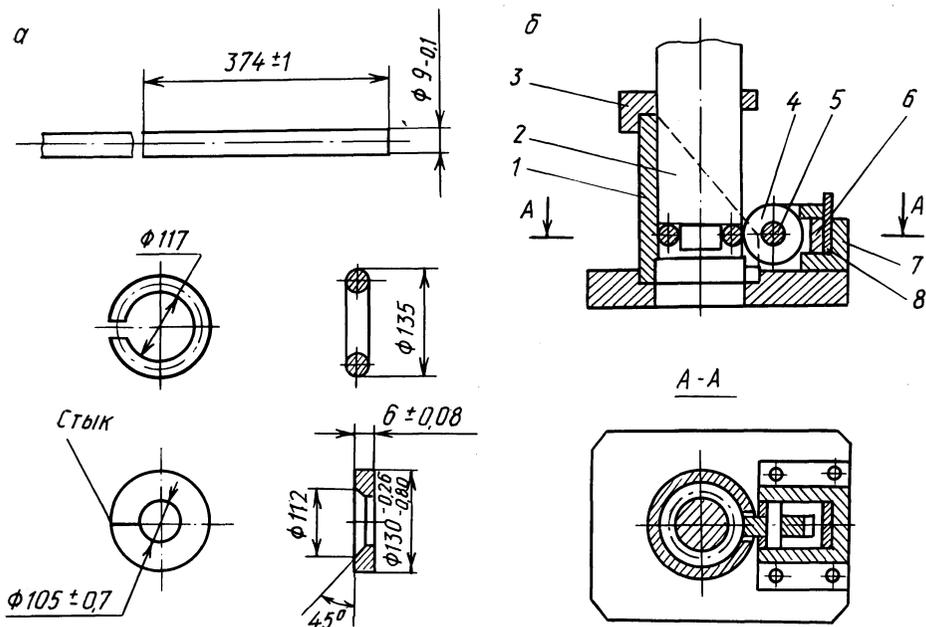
Технология изготовления упорного кольца для трактора "Беларусь" (а) и геликоидальный штамп для гибки кольца (б)
